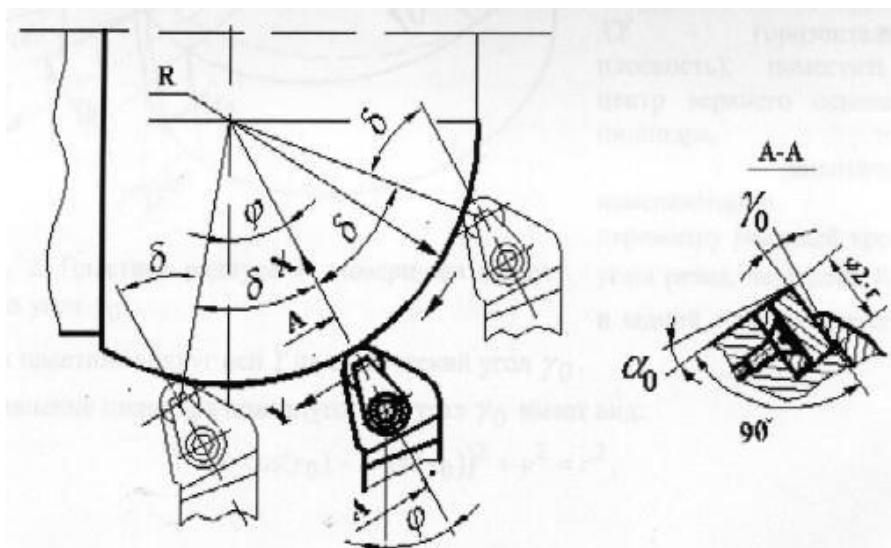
Схема для определения положения вершины резца на контурной линии детали
